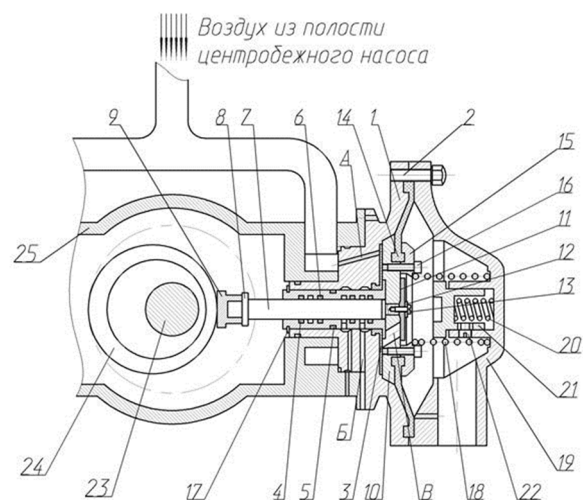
Автоматическая вакуумная система «Primatic»: 1 - корпус вакуумного насоса; 2 - винт; 3 - всасывающий клапан; 4, 5, 6 - кольца уплотнительные; 7 - шток; 8 - шайба; 9 - толкатель; 10 - тарелка; 11 - нагнетательный клапан; 12 - шайба; 13 - винт; 14 - мембрана; 15 - шайба; 16 - винт; 17 - кольцо стопорное; 18 - пружина возвратная; 19 - крышка вакуумного насоса; 20 - пружина контрпоршня; 21 - контрпоршень; 22 - винт; 23 - вал эксцентрика; 24 - эксцентрик; 25 - корпус центробежного насоса; А - всасывающий канал; Б - дренажный канал; В - канал сообщающий полости перед и за мембраной.
